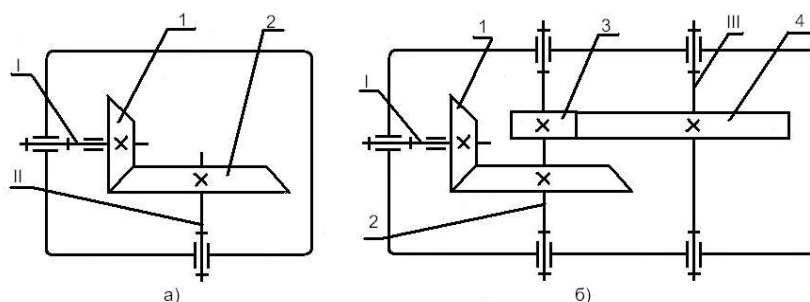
Кінематичні схеми зубчатих механізмів із конічними колесами
